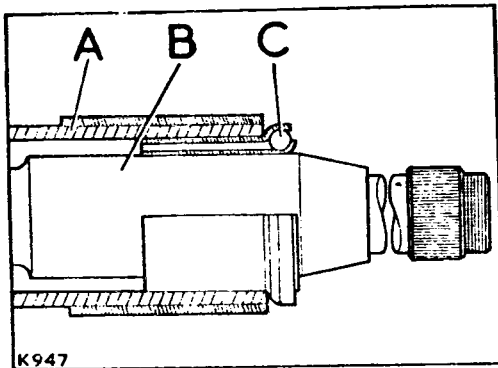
Sección longitudinal de la parte superior de la columna de tipo moderno.
